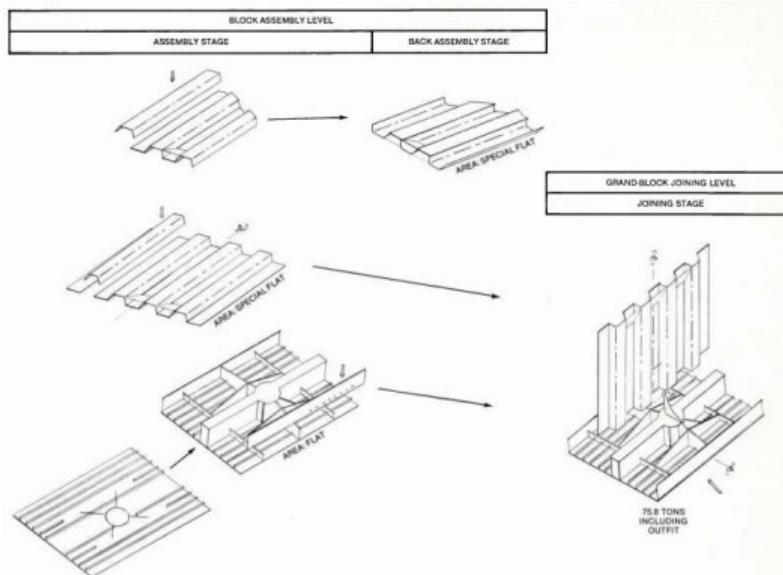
Block Assembly and Grand-block Joining pada Top Wing-tank
